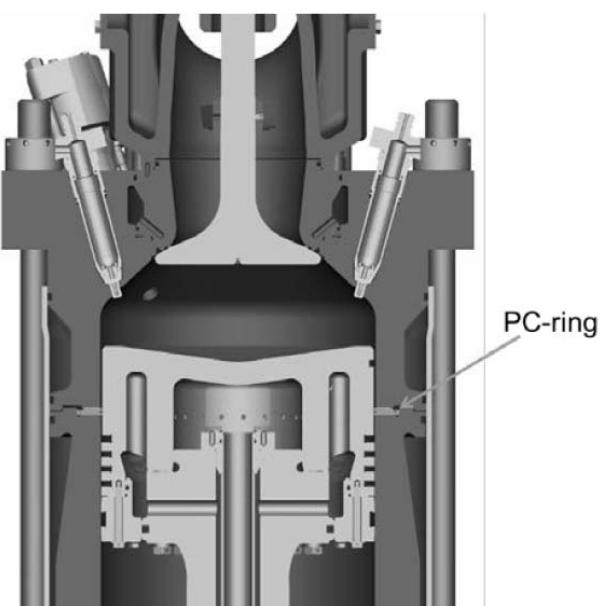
Размещение кольца очистки поршня (PC-ring) между крышкой и втулкой цилиндра
